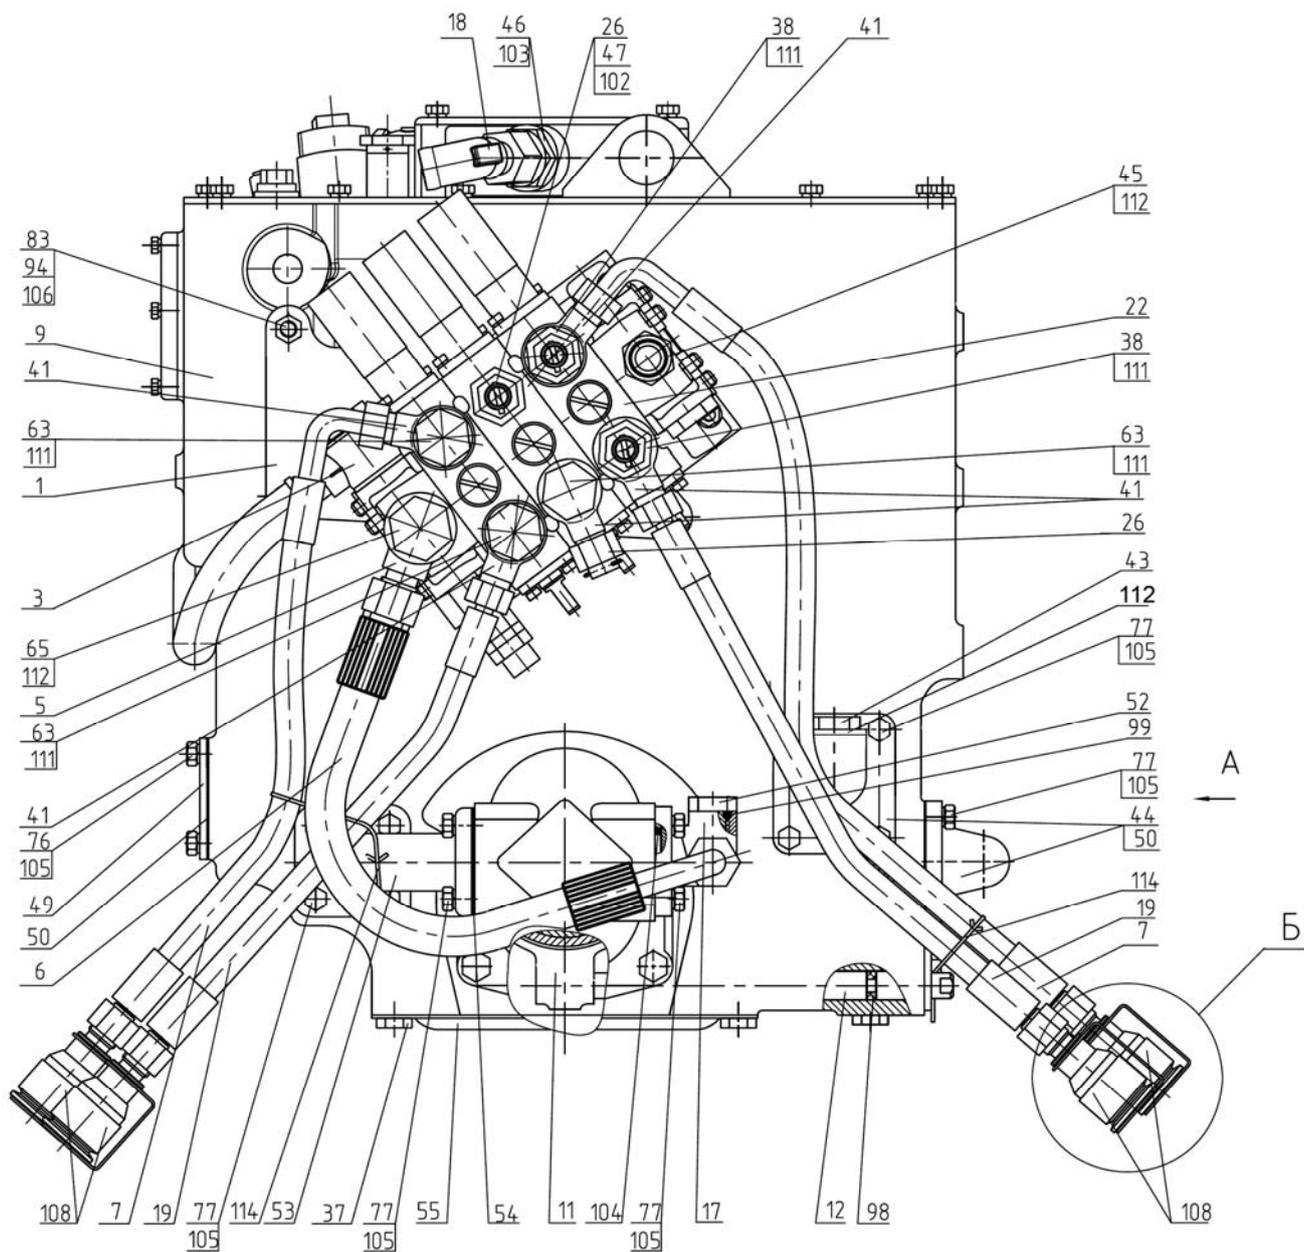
а. Корпус гидросистемы P920-4600015-01
